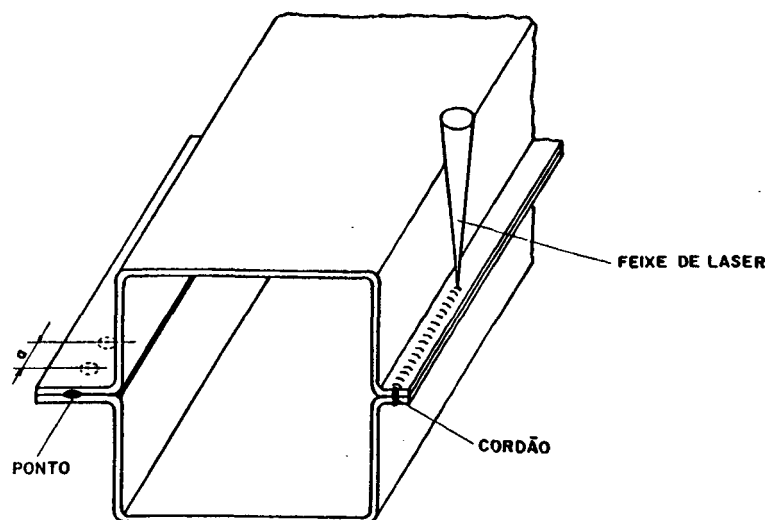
Diminuição da largura da aba na substituição da soldagem a ponto por soldagem a laser.
